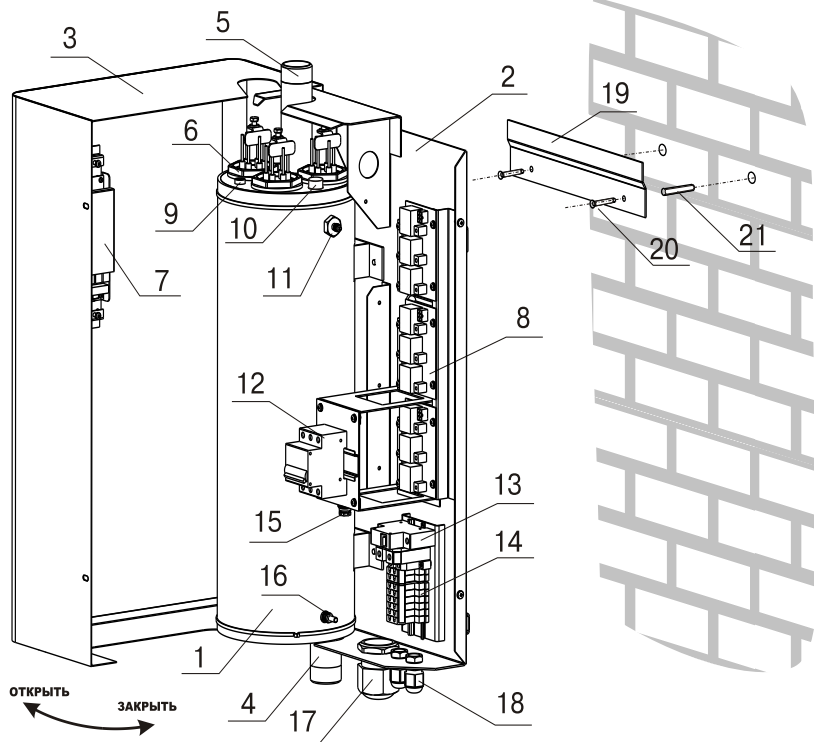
Конструкция водонагревателя и способ его крепления к стене
